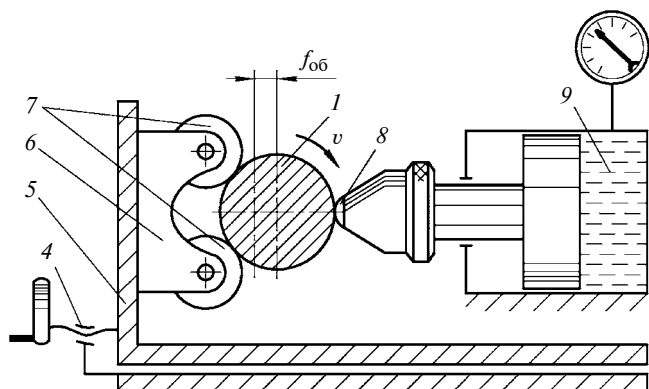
Схема установки для правки ППД с созданием предварительного упругого НДС заготовки:
